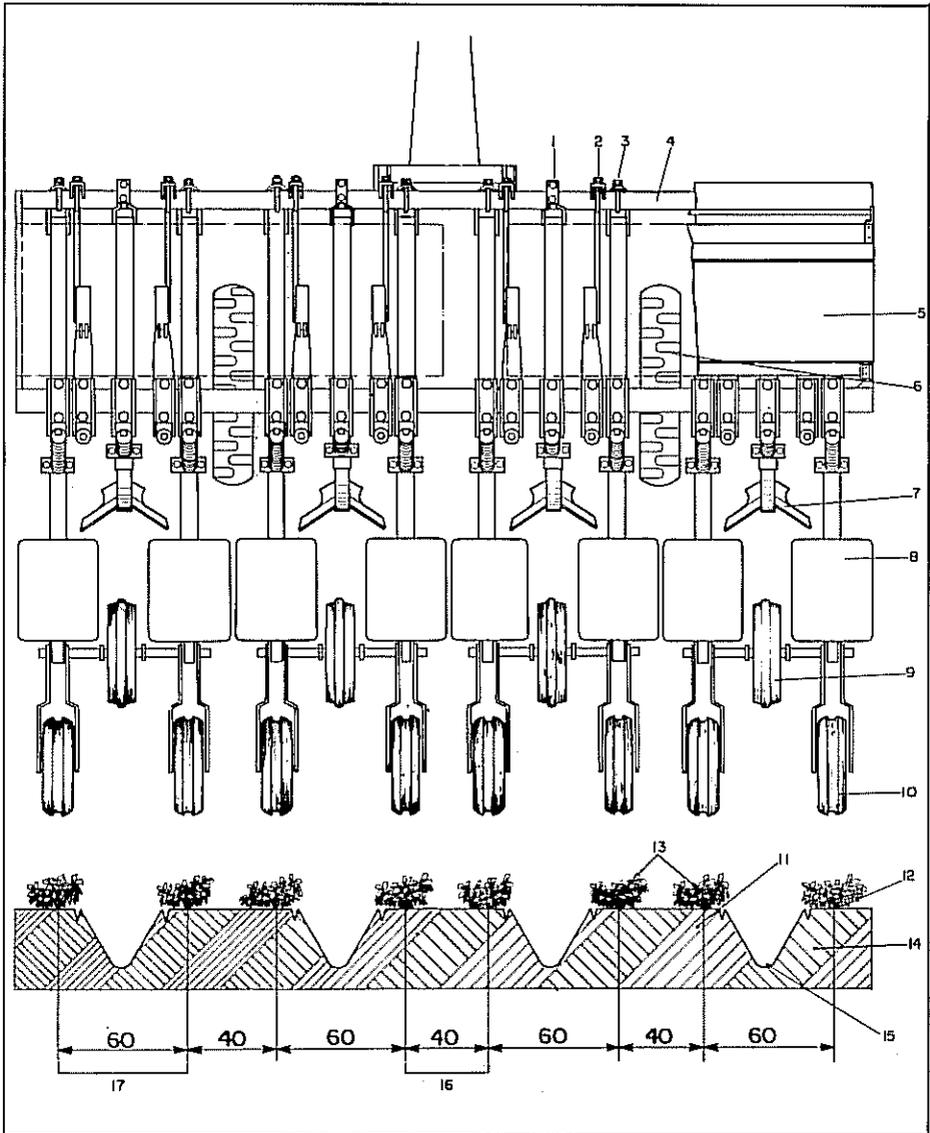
Esquema da plantadeira PP-SOLO 4.000 para plantio de feijão em várzea
